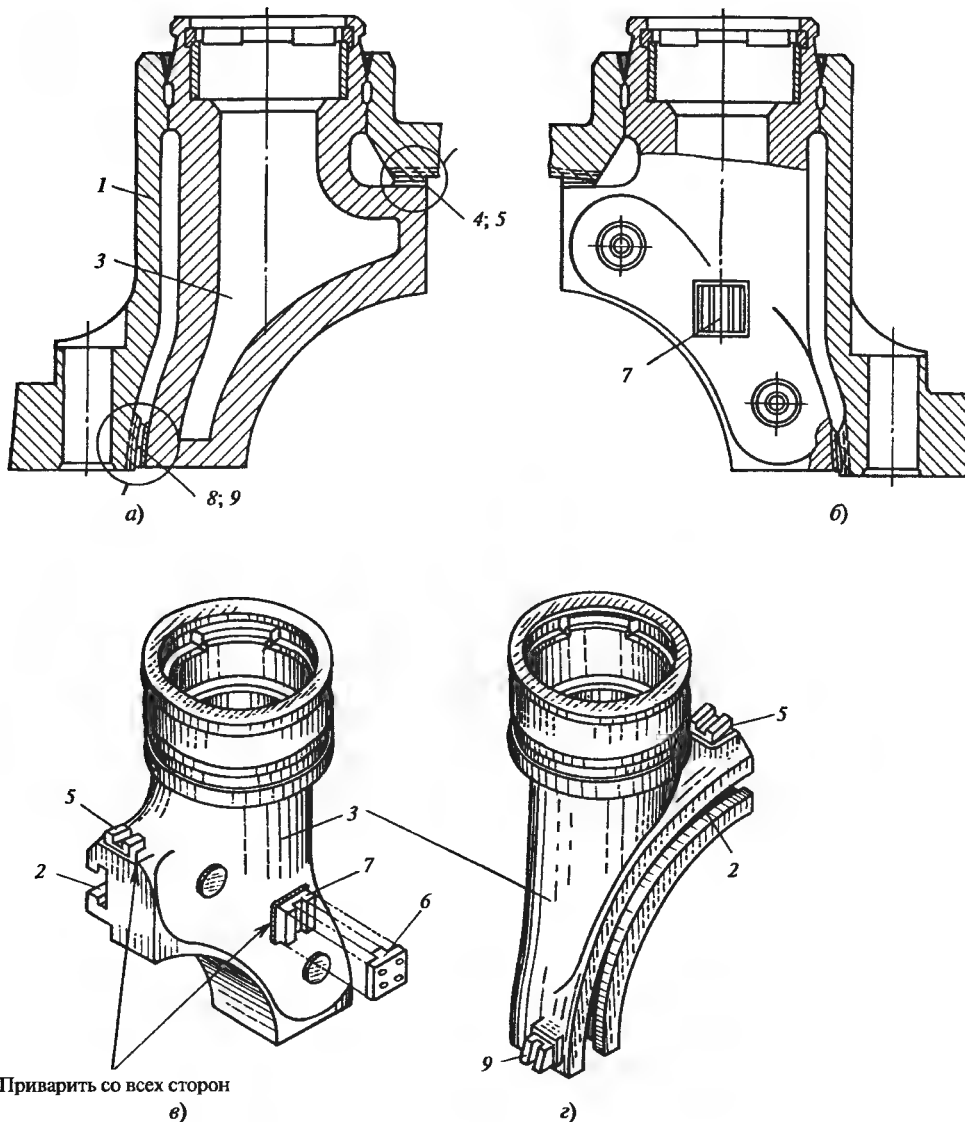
Установка сопловых коробок во внутреннем корпусе двухстенного ЦВД:
